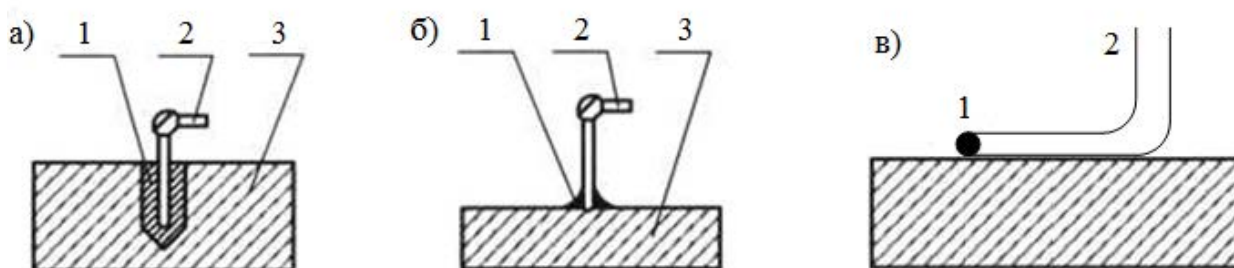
Схемы присоединения термопары к заготовке
